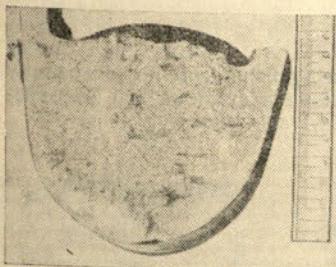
Сечение горизонтального стыка, сваренного ванным способом; разрушение по наплавленному металлу
